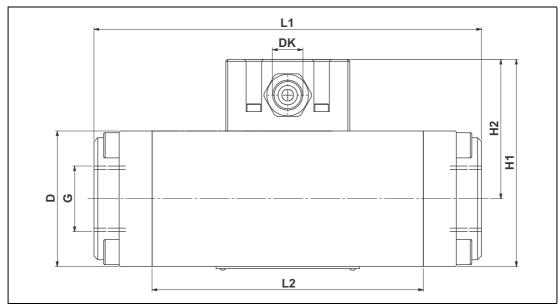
Maßzeichnung OME mit Rohrgewinde
